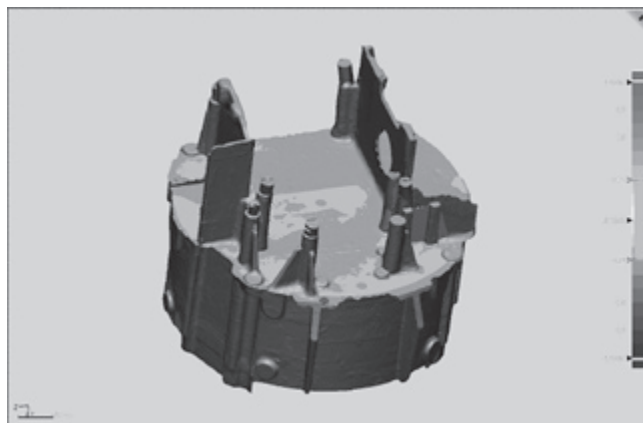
Процесс совмещения CAD-модели теоретической детали с моделью реальной заготовки
